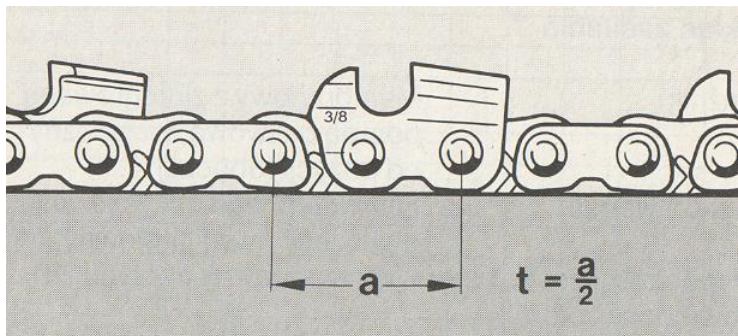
Elementy konstrukcyjne łańcucha:
